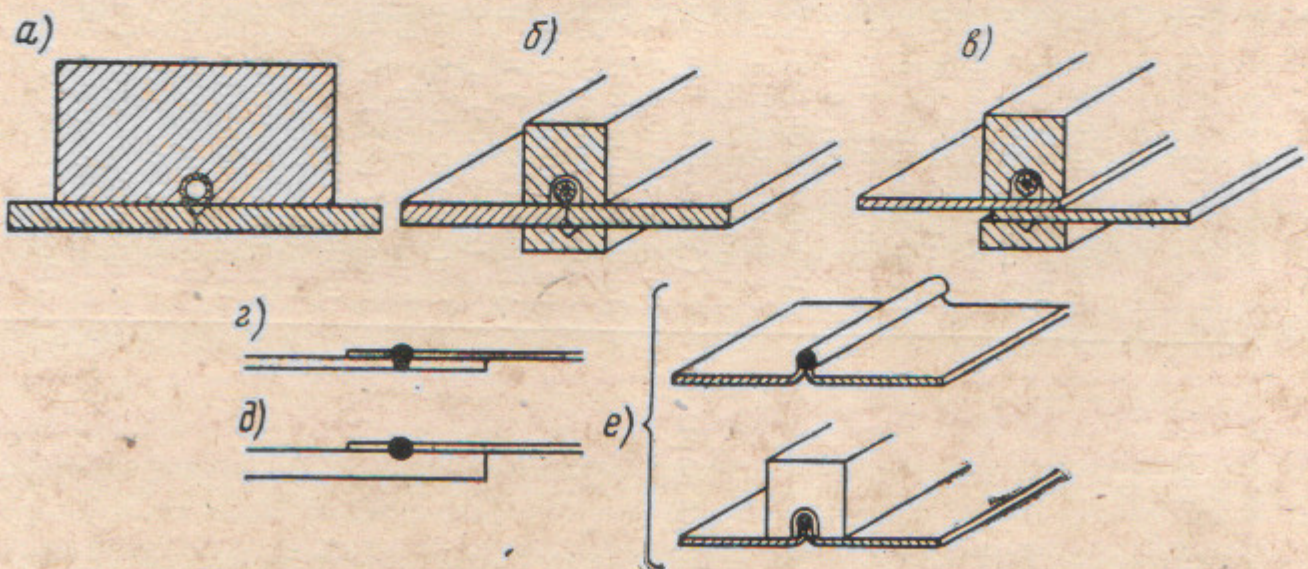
Сварка «лежащим» электродом разных видов (а—е) сварного соединения (см. табл. 1).
